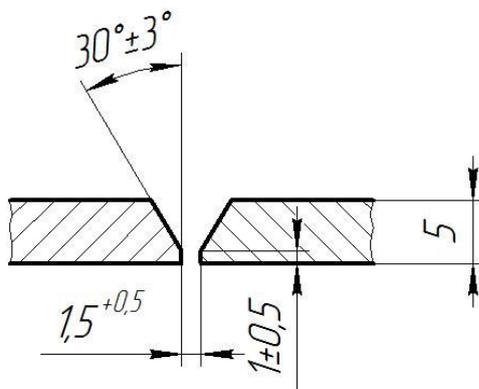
Форма разделки кромок стыковых соединений
